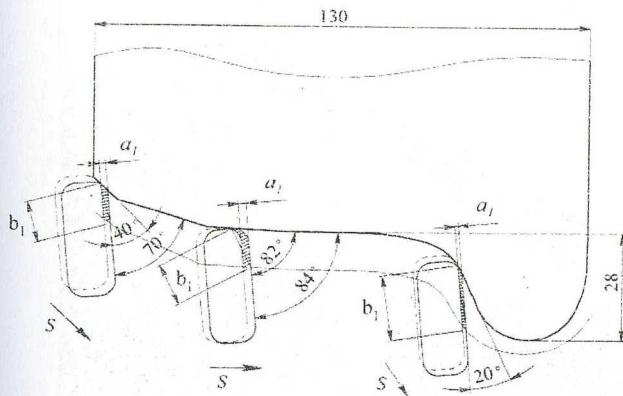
Схема обработки профиля поверхности обода железнодорожного колеса
